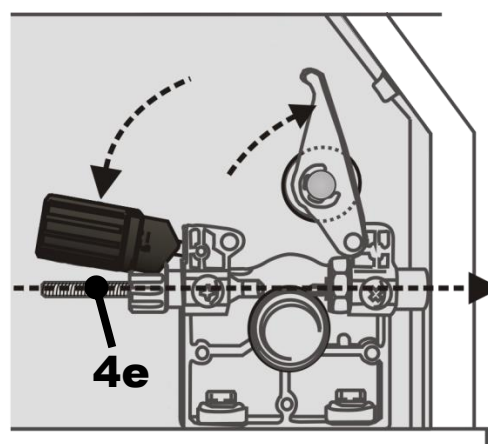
Рисунок E. Устройство механизма подачи сварочной проволоки
